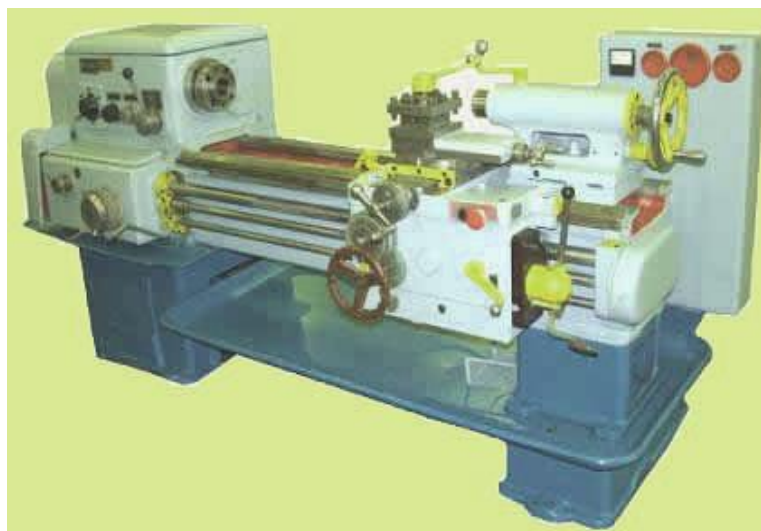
, а – универсальный токарно-винторезный станок 1К62
